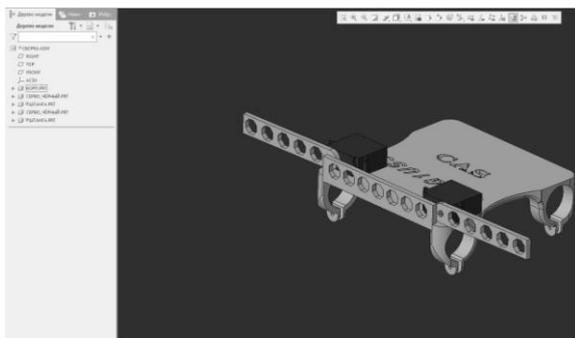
Сборка прототипа с раскрытыми штангами
